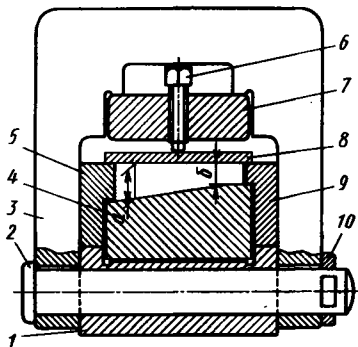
Схема приспособления для сборки под прихватку электросваркой вставок к сегменту:
